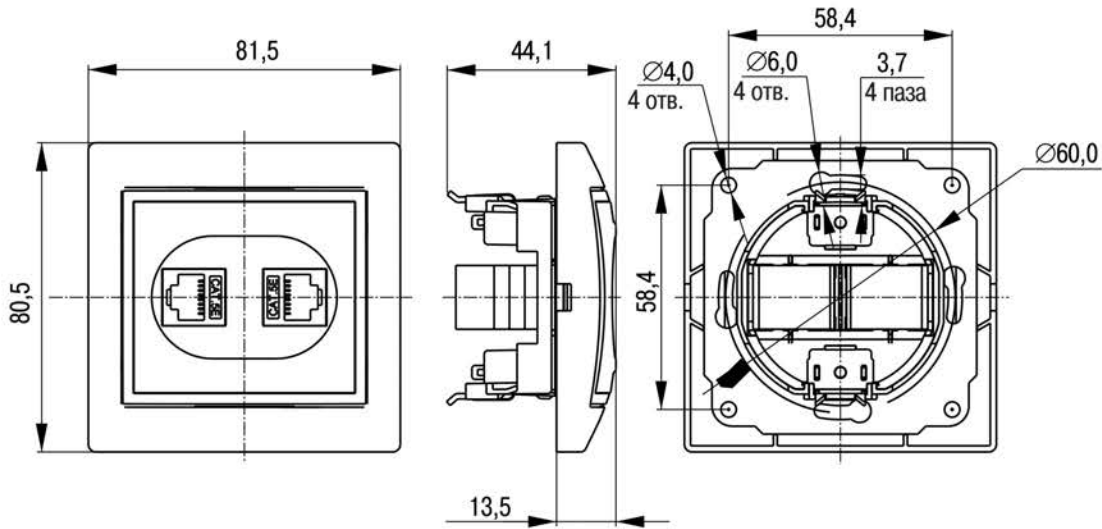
Габаритные и присоединительные размеры РК12-КБ, РК12-ККм
